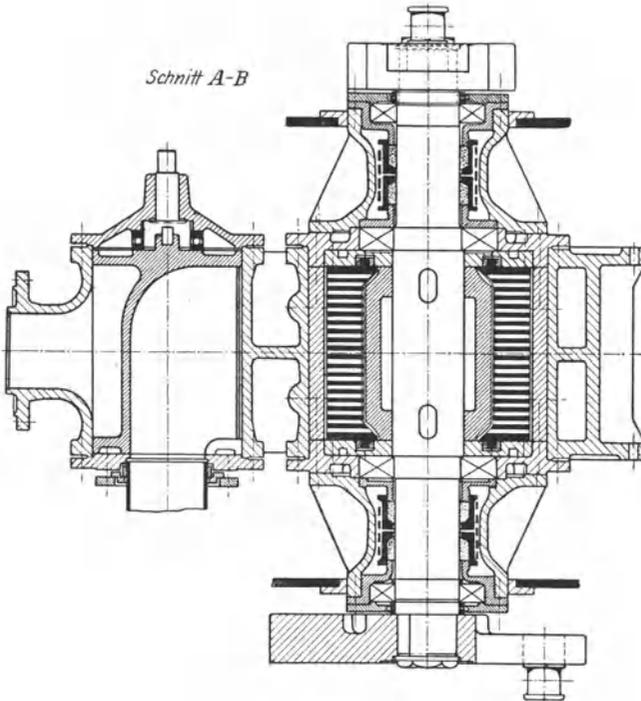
b. Kapselmotor des Lenz-Getriebes. Schnitt *A—B* der Abb. 81 a. (Dieselmaschinen II. S. 72.)
